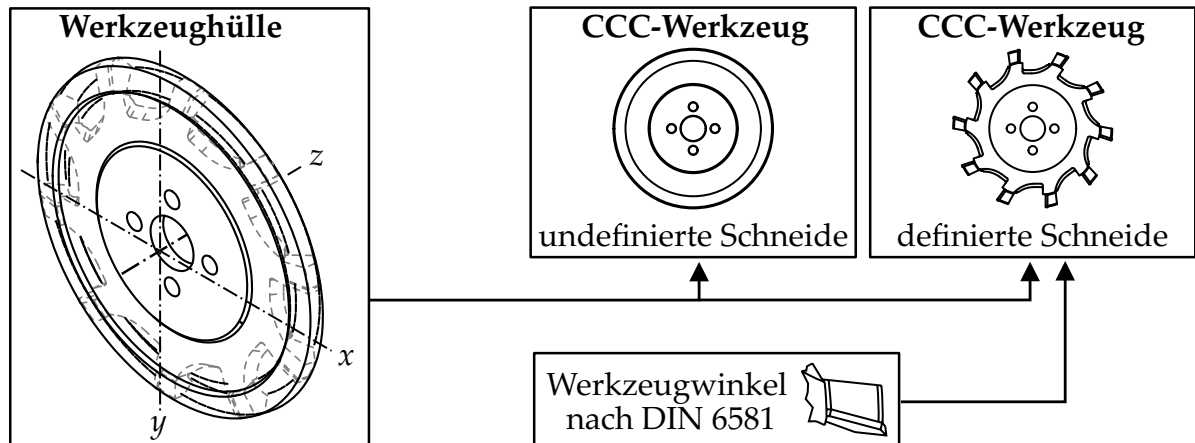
Werkzeughülle zur Beschreibung der Makrogeometrie geometrisch bestimmter und unbestimmter CCC-Werkzeuge
